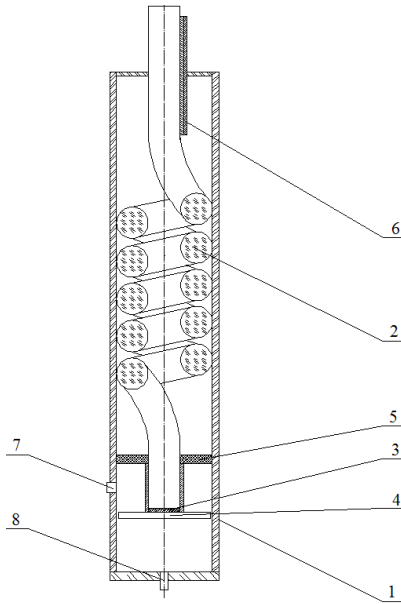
Вимірювач октанового числа легких палив: 1 – корпус; 2 – котушка з волоконного світловода; 3 – віддзеркалюючий шар; 4 – пластина Вільгельмі; 5 – гнучка мембрана; 6 – біметалева пластина; 7 – вхідний отвір для рідини; 8 – вихідний отвір
